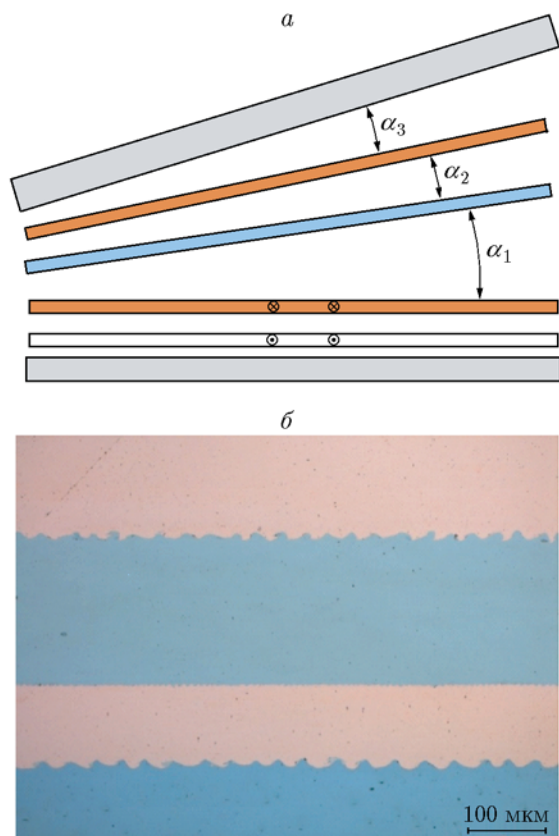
Схема сварки четырех пластин (а). Поперечный шлиф четырехслойного образца Cu—Ni—Cu—сталь Ст.3 (б)
